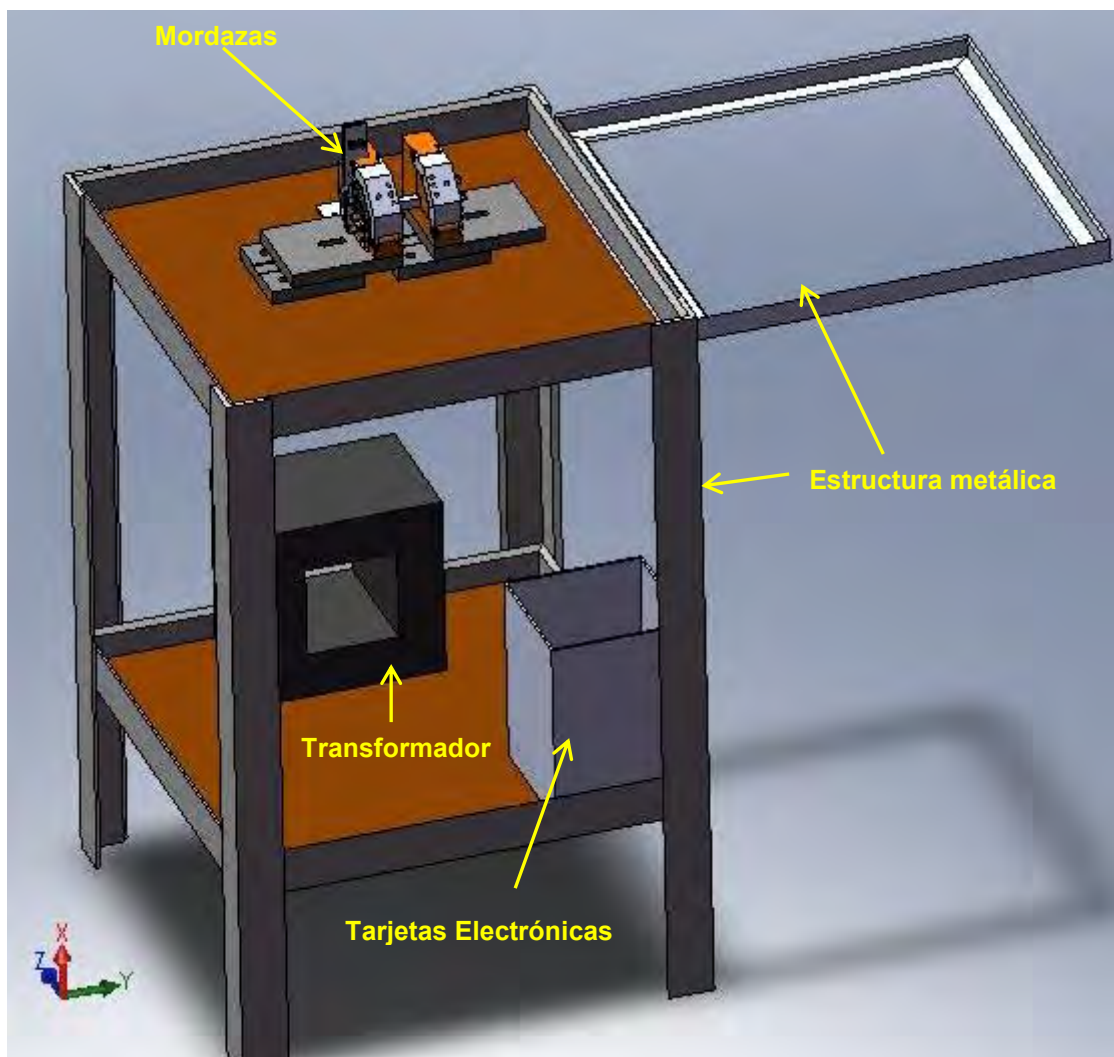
Simulador de ciclo térmico de soldadura
